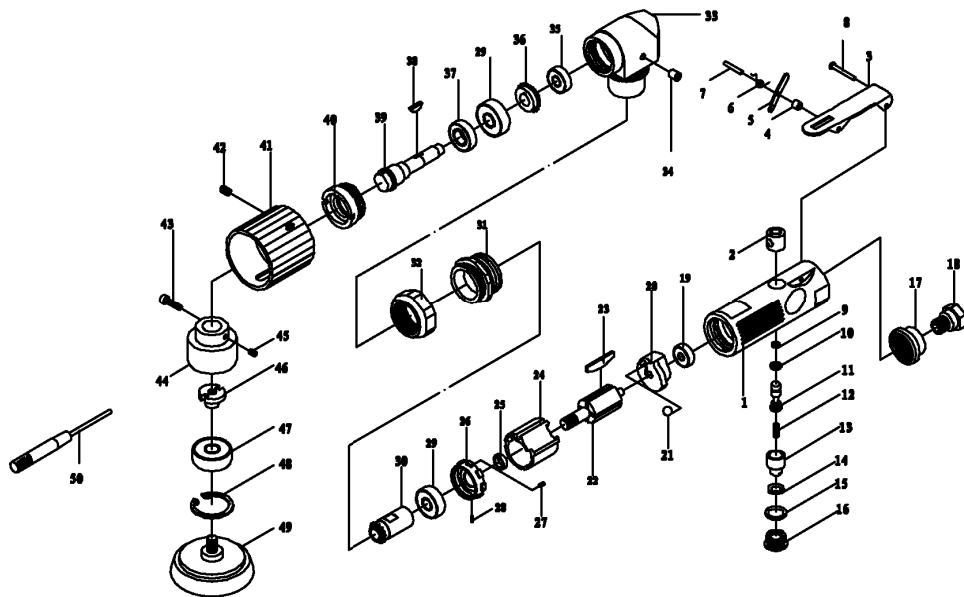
Устройство и схема сборки машины шлифовальной MFG 050/004-2
